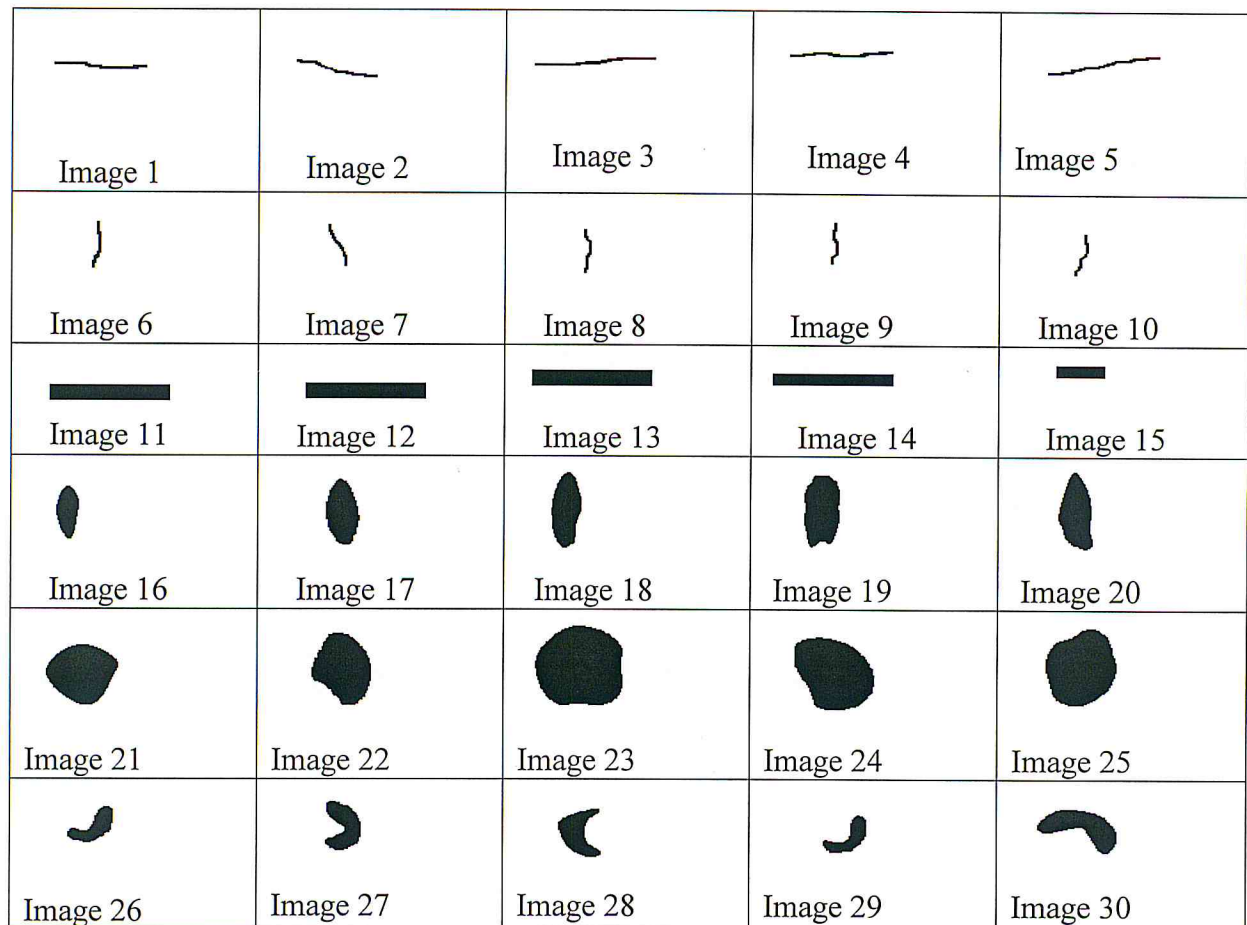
a:Quelque images synthétiques des défauts de joints de soudure
